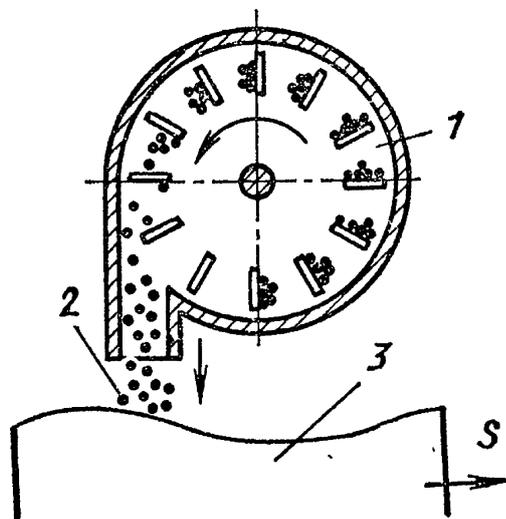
Схема дробеструйной упрочняющей обработки:
